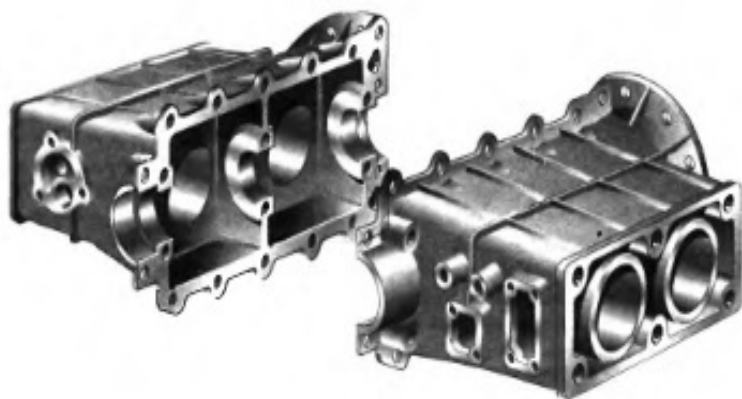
Рознімний блок- картер двигуна з опозитним розташуванням циліндрів.
